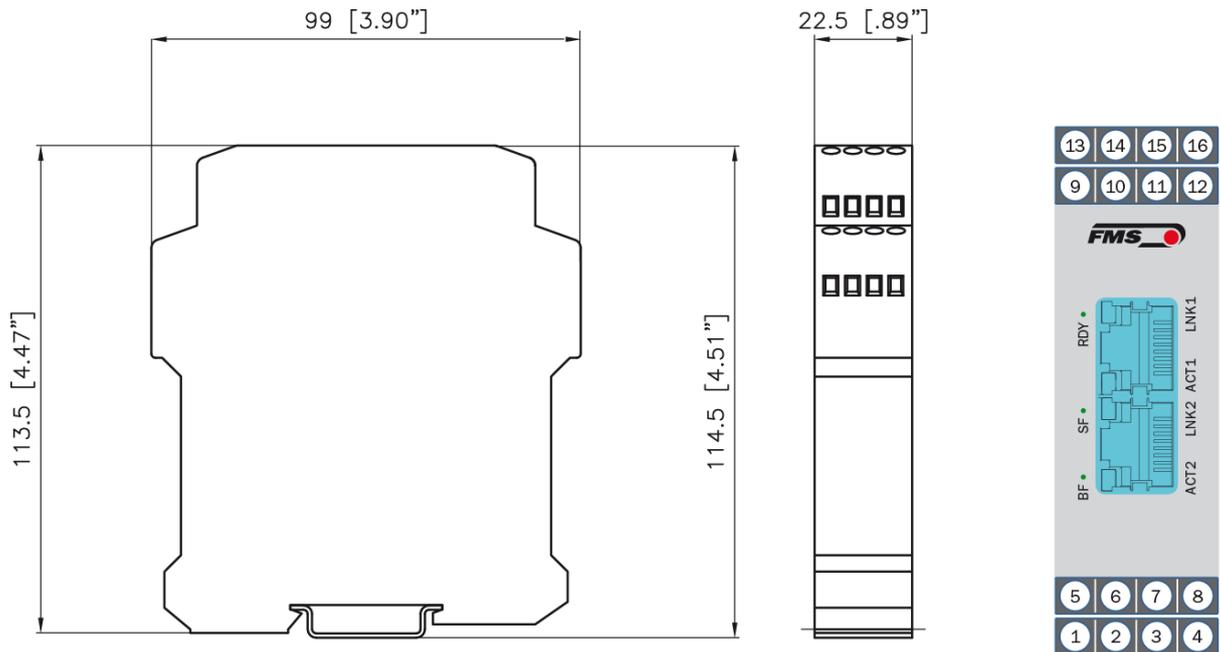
EMGZ490A.R Gehäuse für DIN-Schienenmontage
